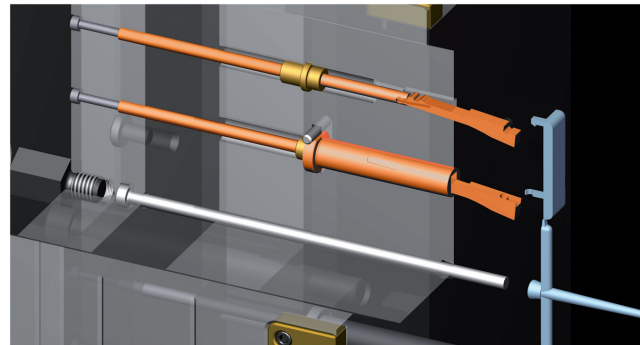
Flexible Auswerfer eingebaut im Spritzgießwerkzeug
